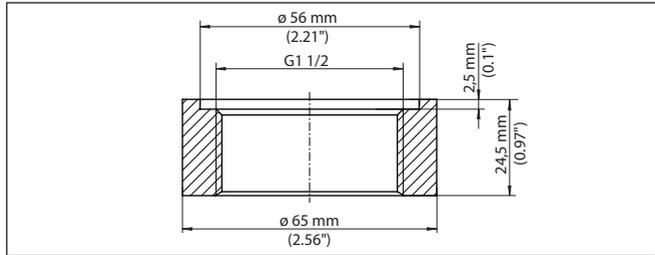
Dimensiones racor para soldar rosca G1½ (DIN 3852-A) - VEGABAR 82, 83, 86, 87
